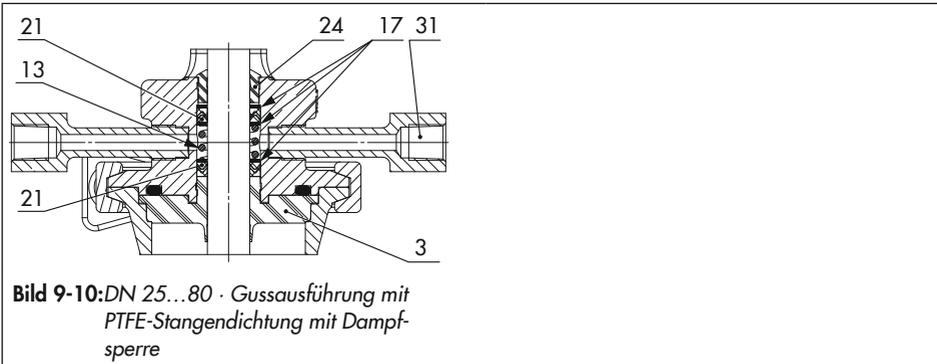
DN 25...80 · Gussausführung mit PTFE-Stangendichtung mit Dampfsperre
